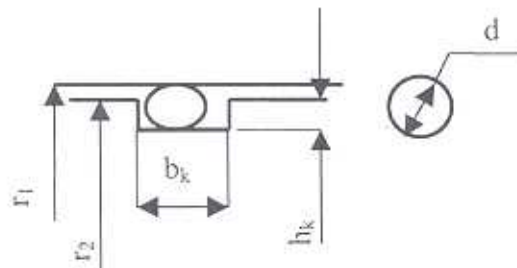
Установка резинового уплотняющего кольца [29]
